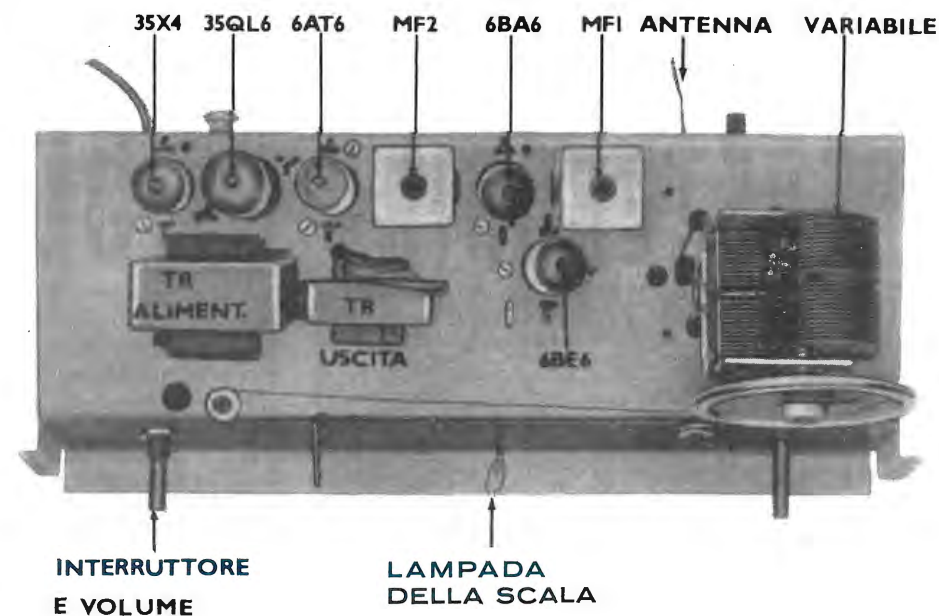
Disposizione meccanica dei componenti sul telaio.
